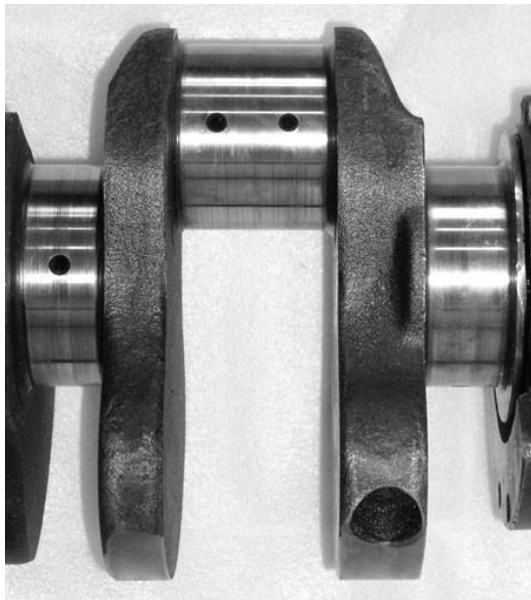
Четверта кривошипна шийка колінчатого вала до руйнування
